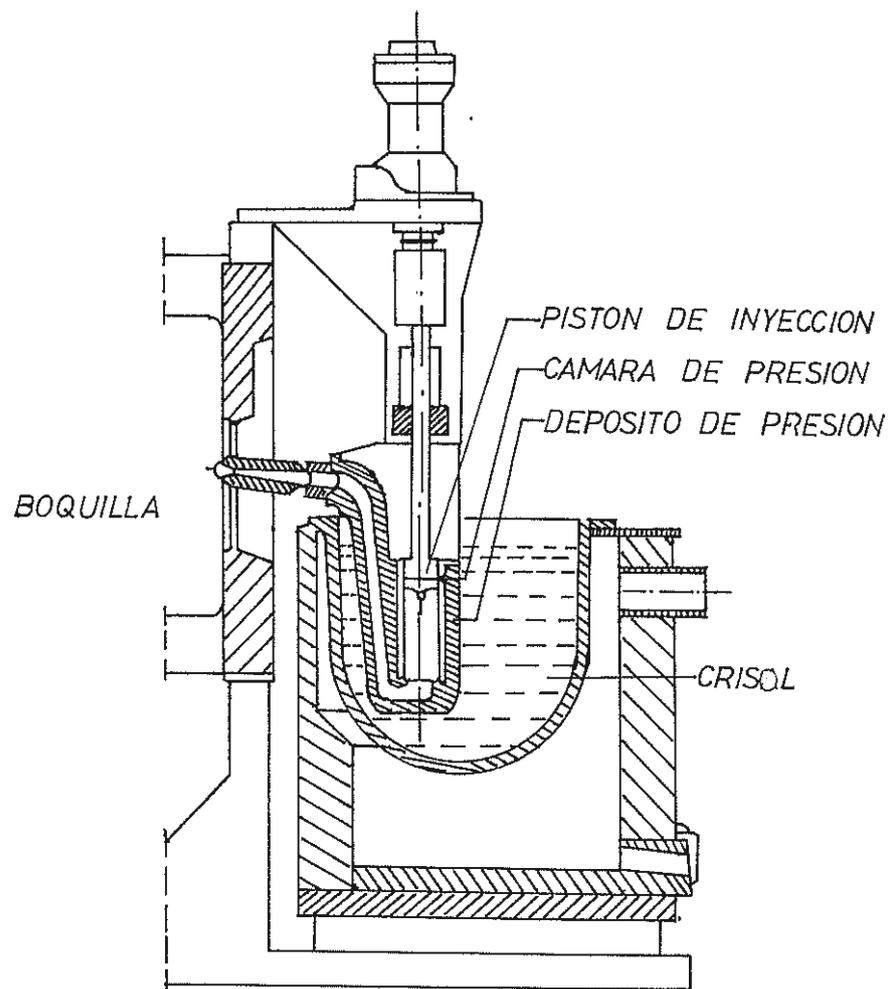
GRUPO DEL PISTON DE INYECCION DE
